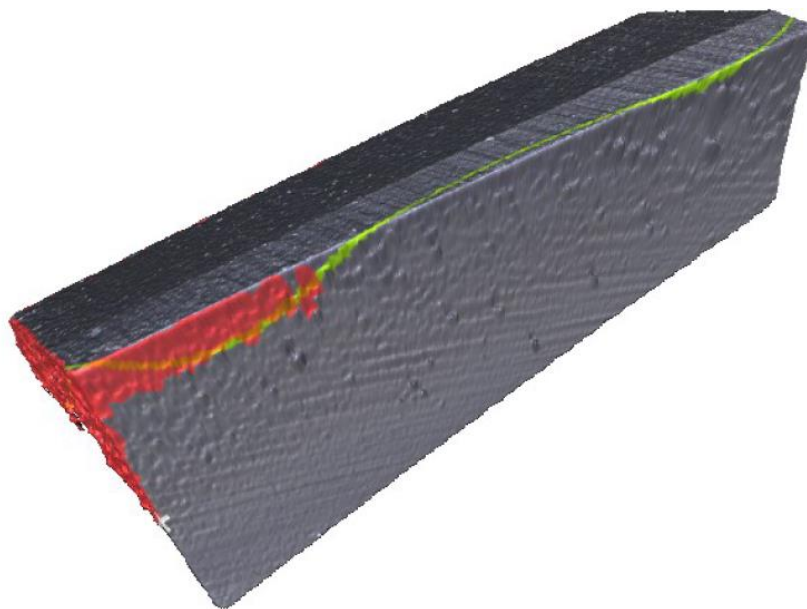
Geometrie břitu frézy ze slinutého karbidu.
